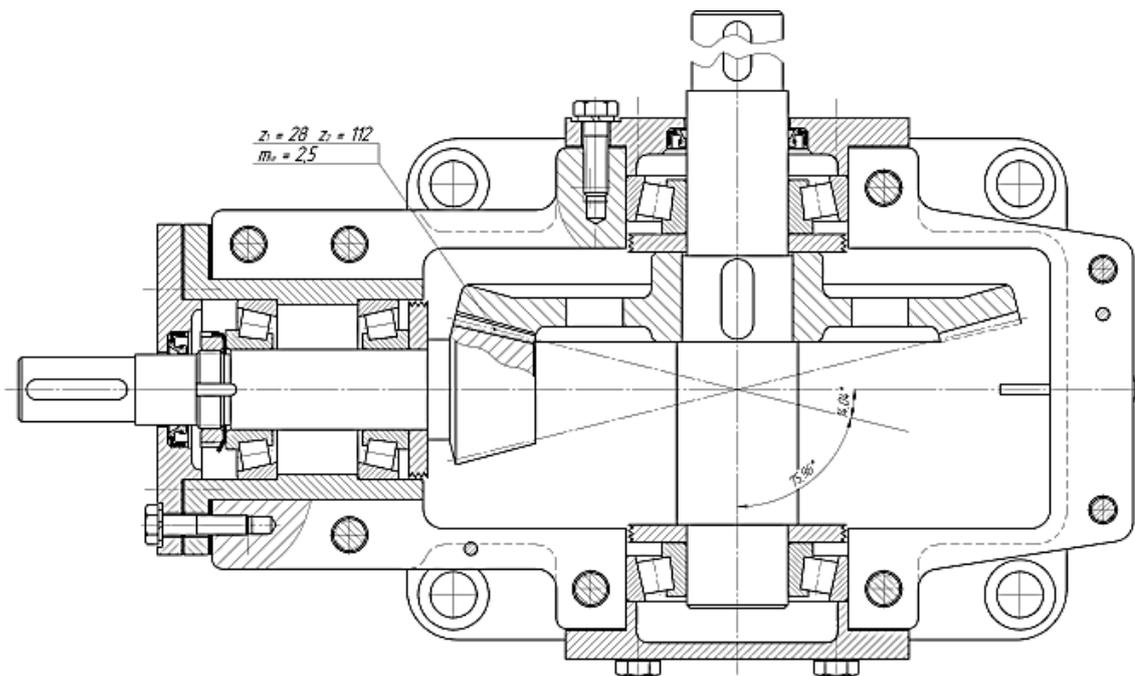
Конический редуктор. Быстроходный вал установлен в растяжку.
